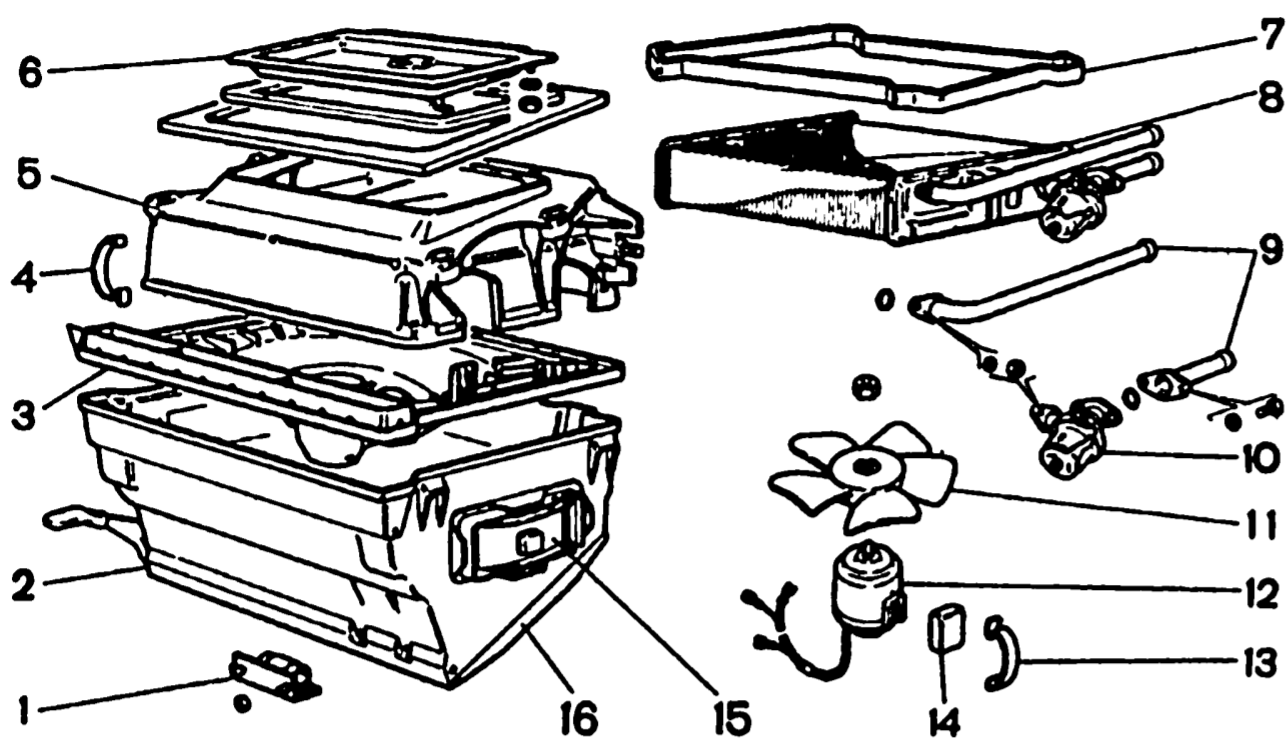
Детали отопителя: 1 - дополнительный резистор; 2 - кожух вентилятора; 3 - кожух направляющий вентилятора; 4 - пружинные скобы; 5 - кожух радиатора; 6 - крышка воздухопритока; 7 - прокладка радиатора; 8 - радиатор; 9 - патрубки; 10 - кран; 11 - крыльчатка; 12 - электродвигатель; 13 - пружинная скоба вентилятора; 14 - подушка электродвигателя; 15 - заслонка; 16 - воздухораспределительная крышка
